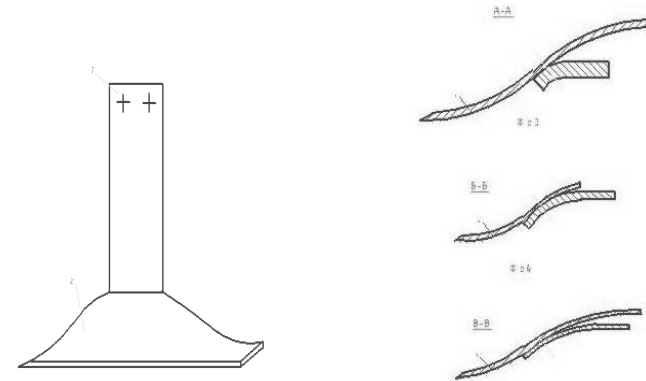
Робочий орган для обробки ґрунту, вид збоку
